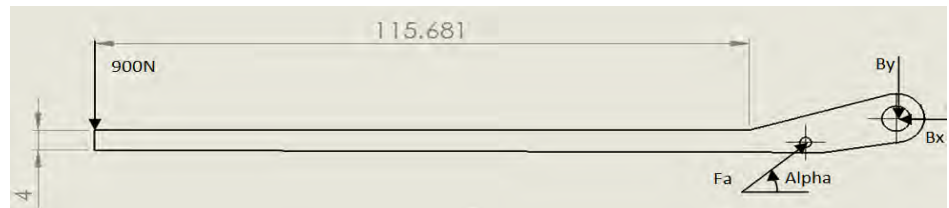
Mecanismo usado para el proceso de monte y desmonte de la herramienta.
